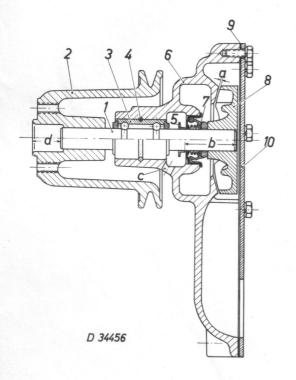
Montage à la presse de la turbine - Mesure de la distance.
